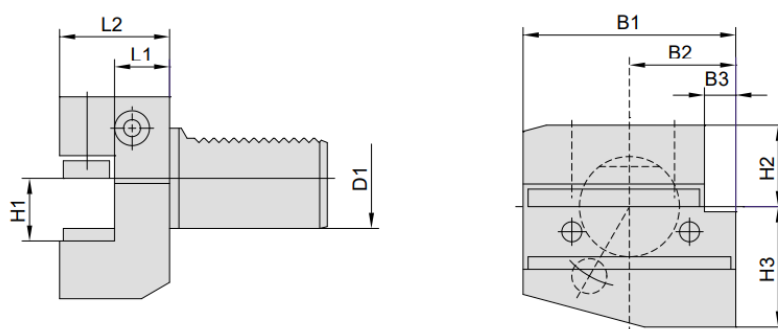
Резцедержатель DIN 69880 48-B1-40x20
